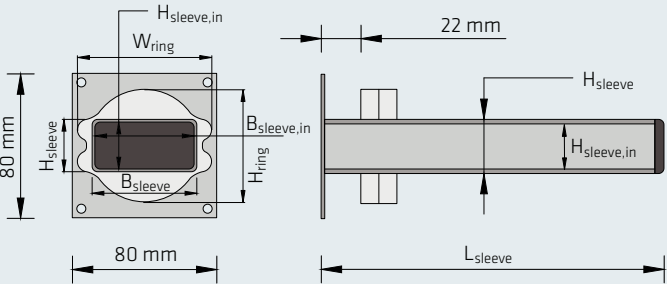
Rück- und Seitenansicht ESD-Q-Hülse
